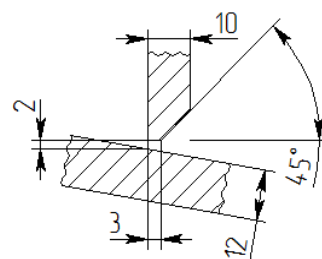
Вид з'єднання і конструктивні розміри зварного таврового шва ГОСТ 23518-79, ТЗ
